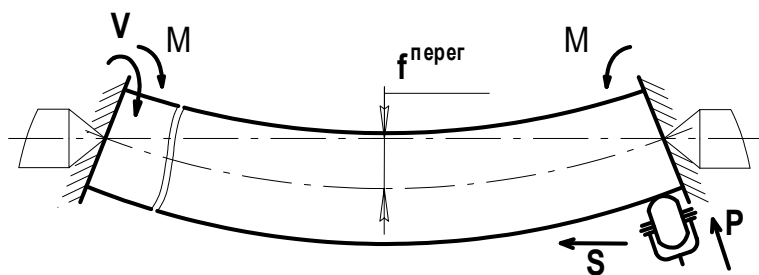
Схема правки ППД вращающейся упругодеформированной заготовки
